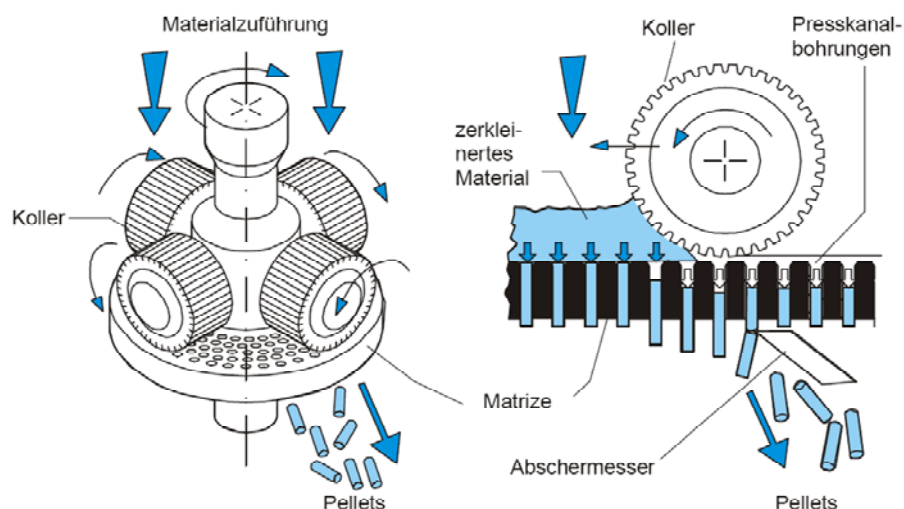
Arbeitsprinzip einer Pelletpresse mit Flachmatrize /103/
